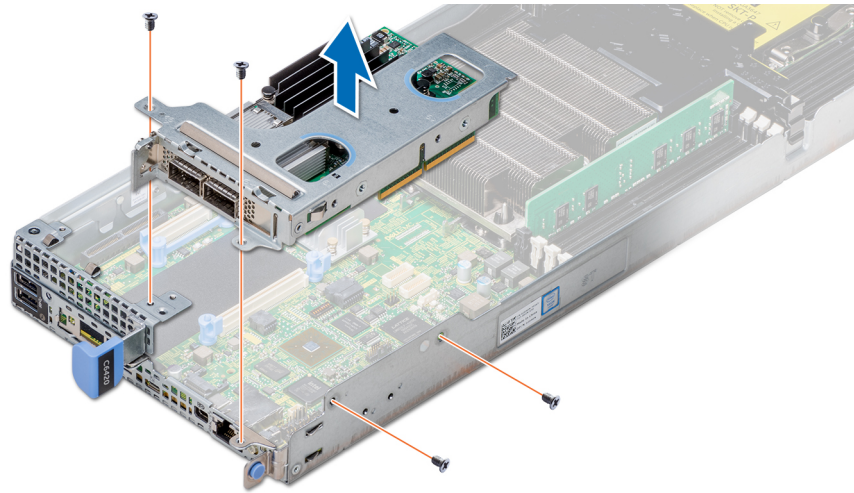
Retrait de l'assemblage de la carte de montage pour carte d'extension
